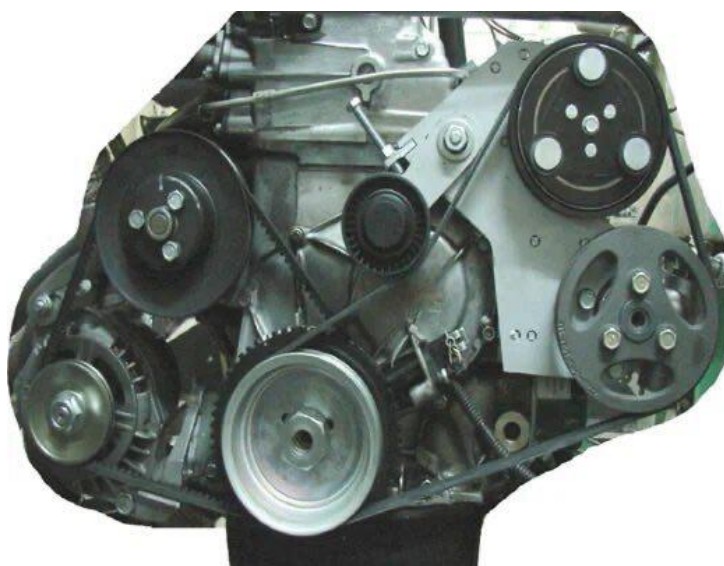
Привод вспомогательных агрегатов двигателя ВАЗ 21214
